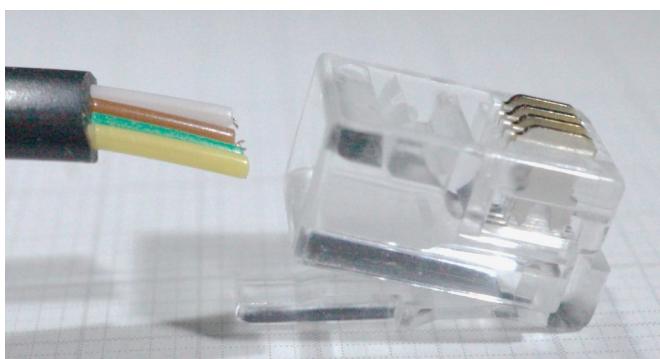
Motorstecker: Kabel in Modular 4P4 Stecker einführen - POLUNG !!!
